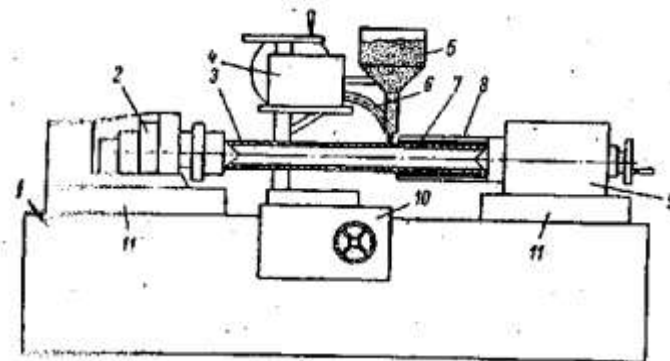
Установка для автоматичної наплавки деталей під шаром флюса:
